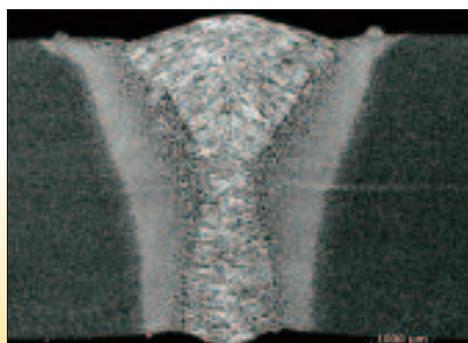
Coupe métallographique d'une soudure laser Nd:YAG - MAG hybride sur acier inoxydable austénitique AISI 304 de 3 mm d'épaisseur, réalisée en une passe avec une vitesse de 3,6 m/min par VITO
